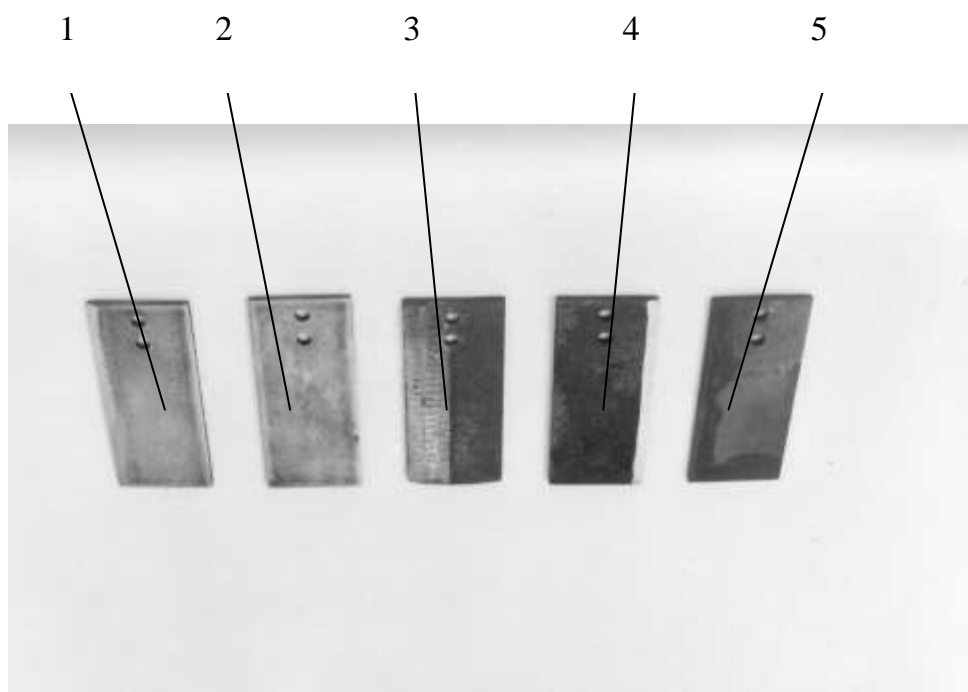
Загальний вигляд лабораторних зразків для проведення лабораторних досліджень на зношування: незагартовані зразки: загострений (1) та незагострений (2); зміцнений наварюванням кераміко-металевої композиційної стрічки (3); загартовані зразки: загострений (4) та незагострений (5)
